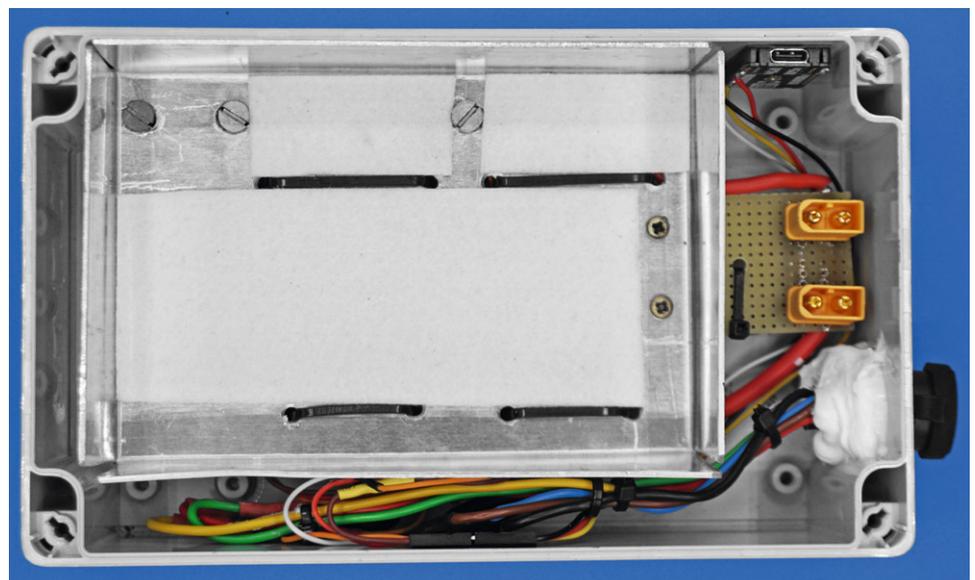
Montage der Motoranschlussbuchse und der anderen Komponenten
